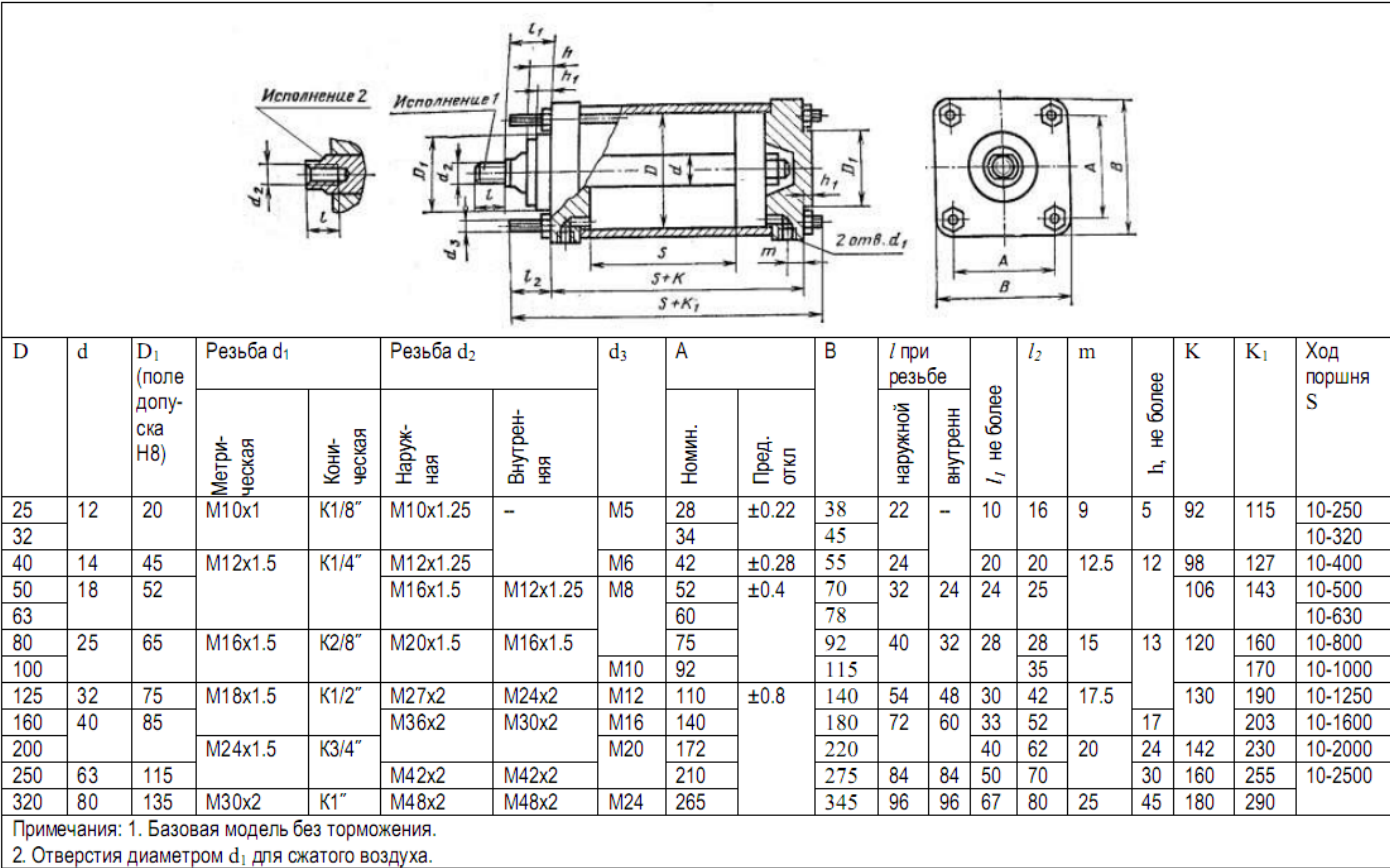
Пневмоцилиндры без торможения, размеры
